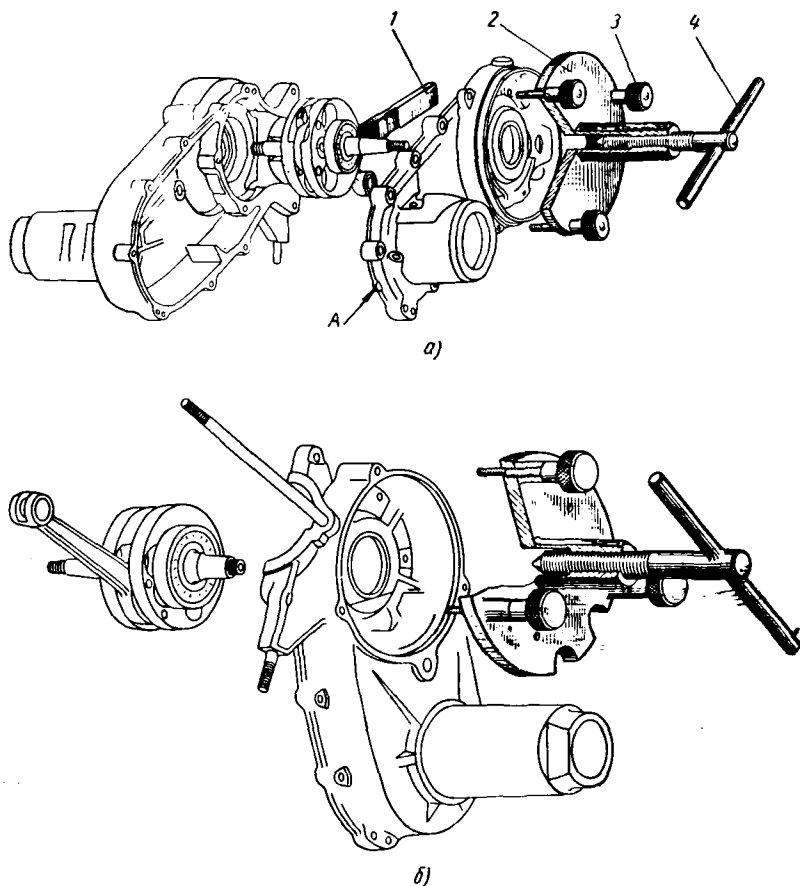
Разъединение картера двигателя с помощью клина и съемника:
